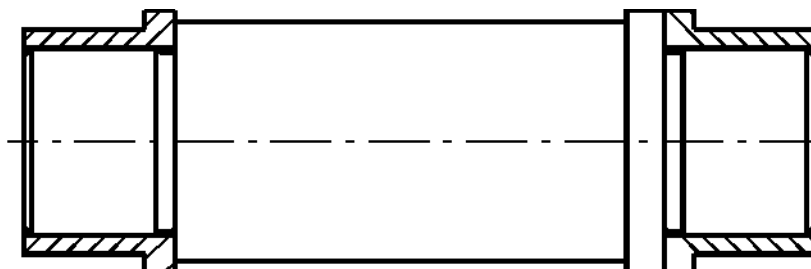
Реализация двойной направляющей базы сочетанием двух цилиндрических поверхностей
